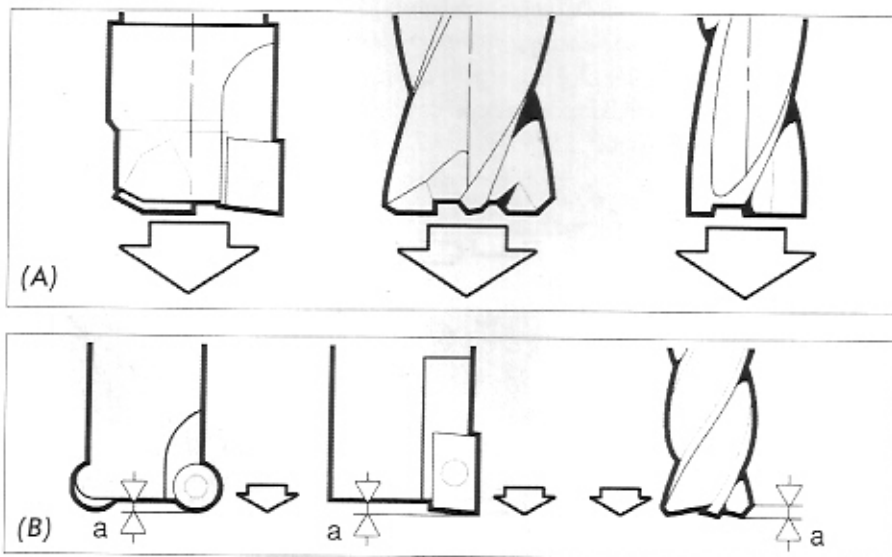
Fresas Frontais para a Usinagem de Bolsões
